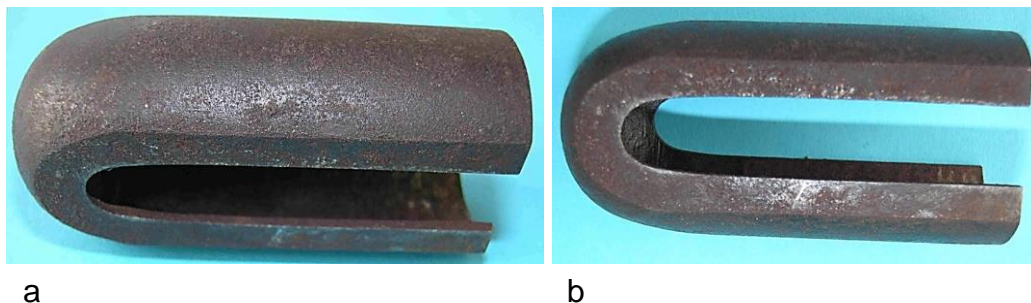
Zweipoliger Tulpenmagnet (Länge 75 mm, Magnetdicke 5mm): a) Sichtbare Außenfläche, b) Geschliffene Seiten des Magneten
